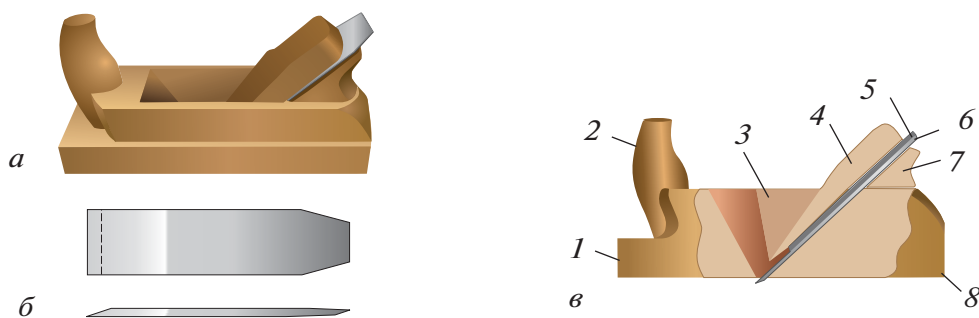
Рубанок с деревянной колодкой: *а* — общий вид рубанка; *б* — железка (нож); *в* — основные части рубанка: 1 — колодка; 2 — передняя ручка-рожок; 3 — леток; 4 — деревянный клин; 5 — стружколом; 6 — нож; 7 — упор; 8 — подошва
